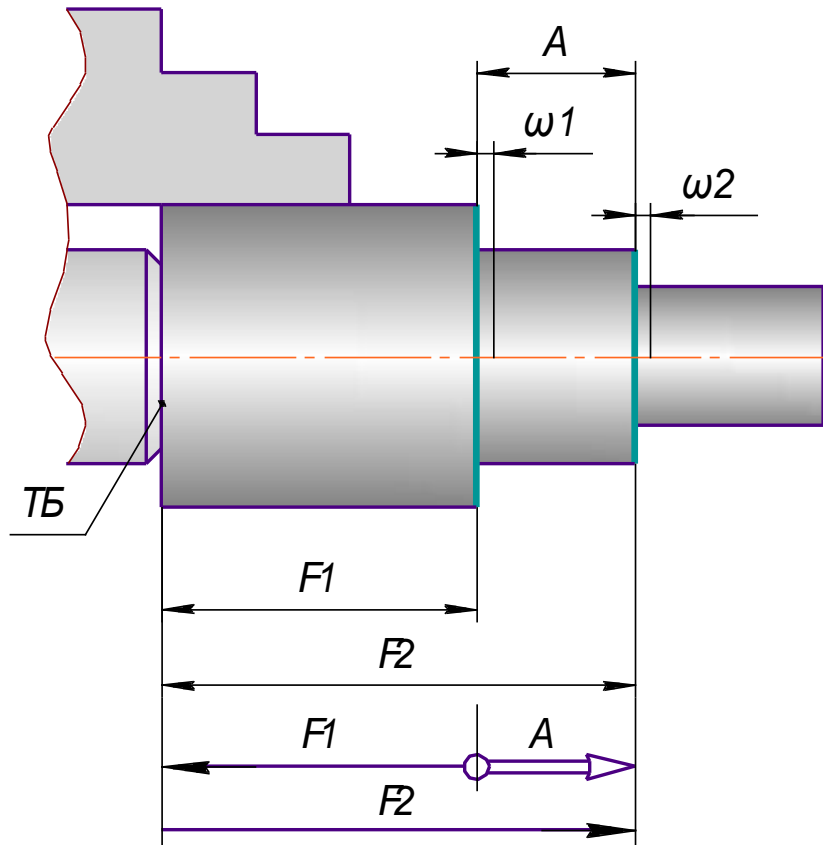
Ескіз та розмірний ланцюг токарної обробки деталі “Вісь”
